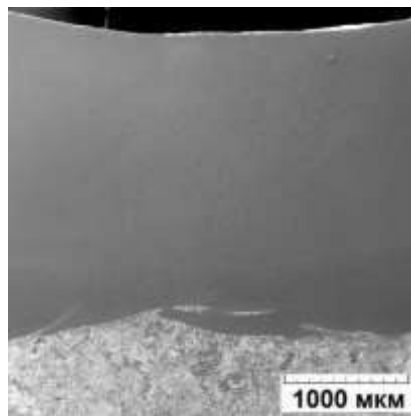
Макрошліф металізаційного покриття після плазмового оплавлення
